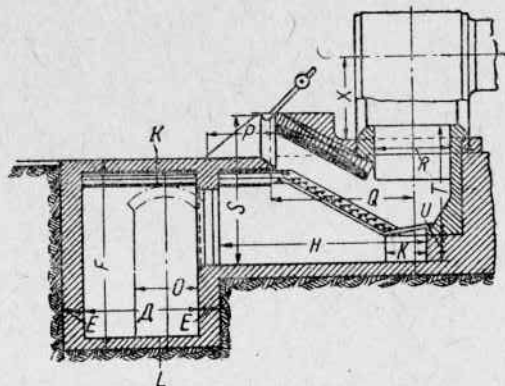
Ступенчатая топка для котла паровозного типа локомотива класса А и Д для мелкого топлива.
